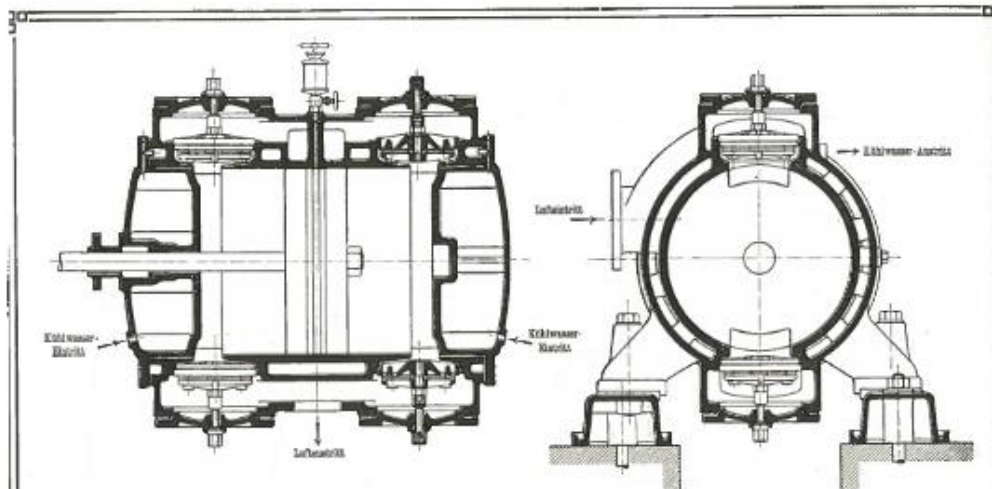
Längs- und Querschnitt des Luftzylinders.
